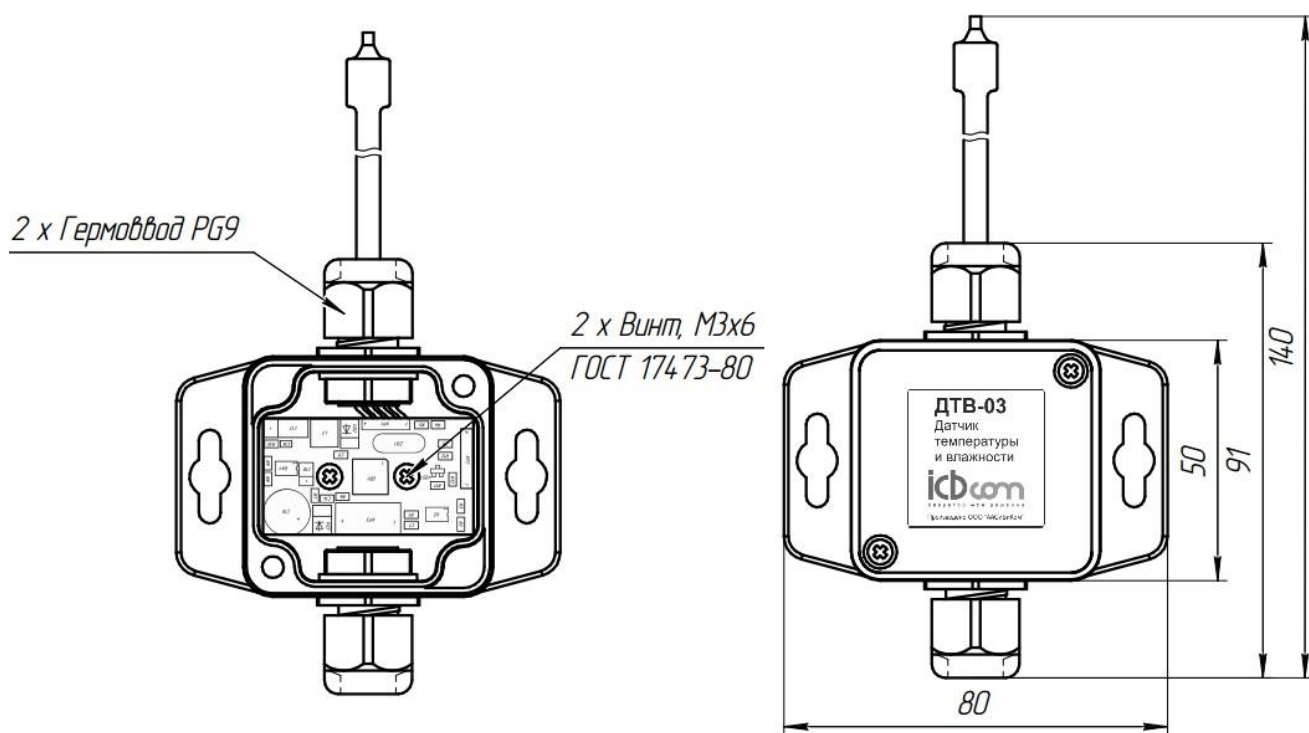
Схема и габаритные размеры ДТВ-03
